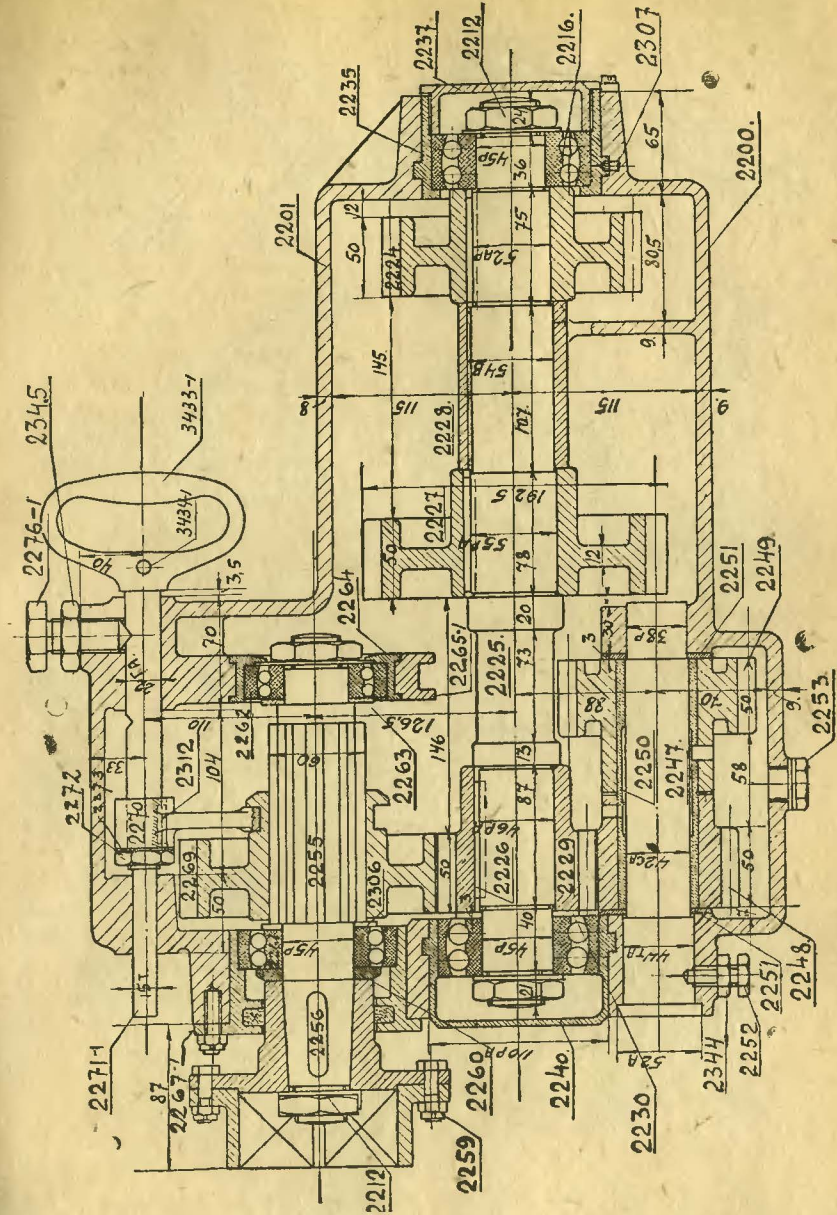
Коробка скоростей (вид сверху, крышка снята)
